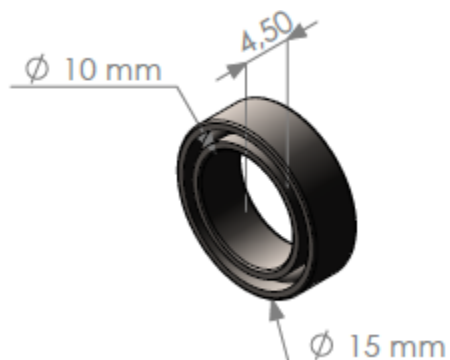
Vista isométrica de rodamiento 0100-15.
